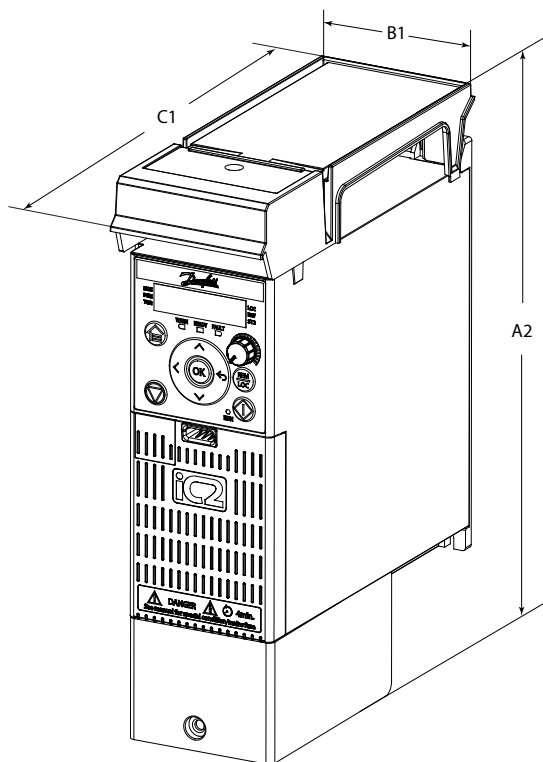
Розміри й габарити корпусів IP21/UL, Тип 1
